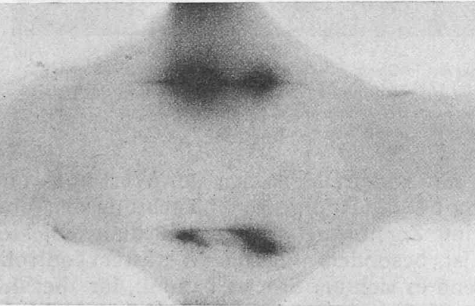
Röntgenaufnahme einer Doppelkehlnaht. Bindefehler und mangelhaftes Aufsitzen der aufgeschweissten dünnern Bleche sind deutlich wahrzunehmen. Durchleuchtete Materialstärke 60 mm Eisen.
